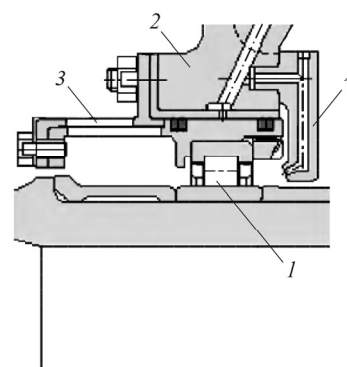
Подача масла между внутренним кольцом подшипника и сепаратором: 1 – ролик-подшипник; 2 – корпус; 3 – упруго-демпферная опора; 4 – форсунка
